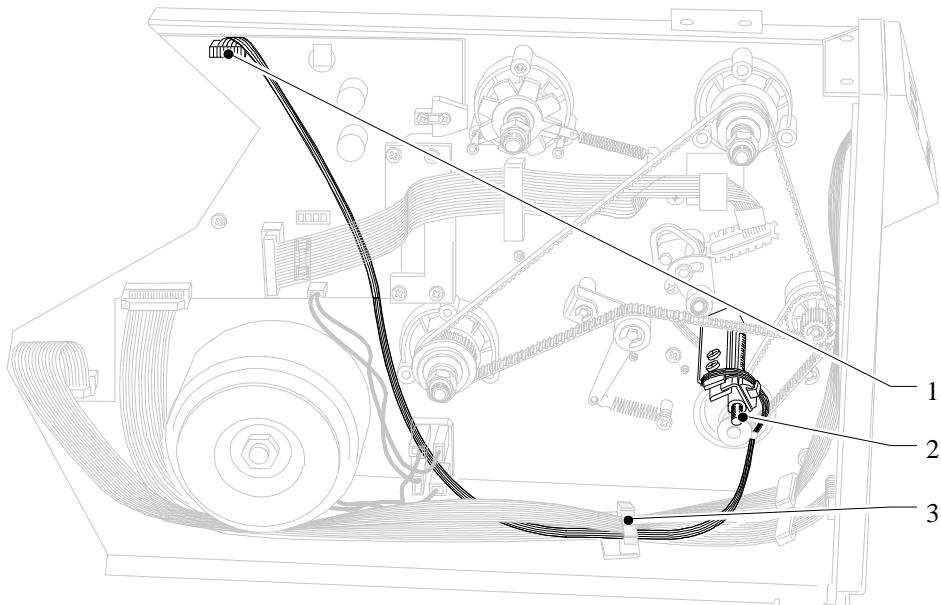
1 Kabelstecker der Etikettenlichtschranke
